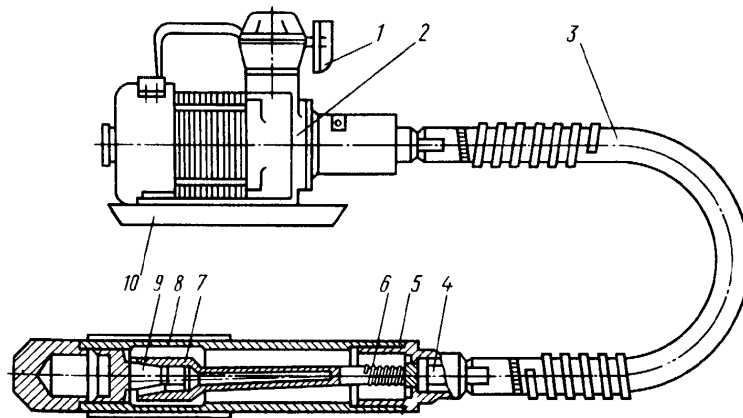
Ручной глубинный вибратор с гибким валом: 1 – выключатель; 2 – электродвигатель; 3 – броня гибкого вала; 4 – гибкий вал; 5 – наконечник, 6 – пружинная муфта; 7 – дебаланс; 8 – корпус вибратора; 9 – конус; 10 – металлическая подставка
